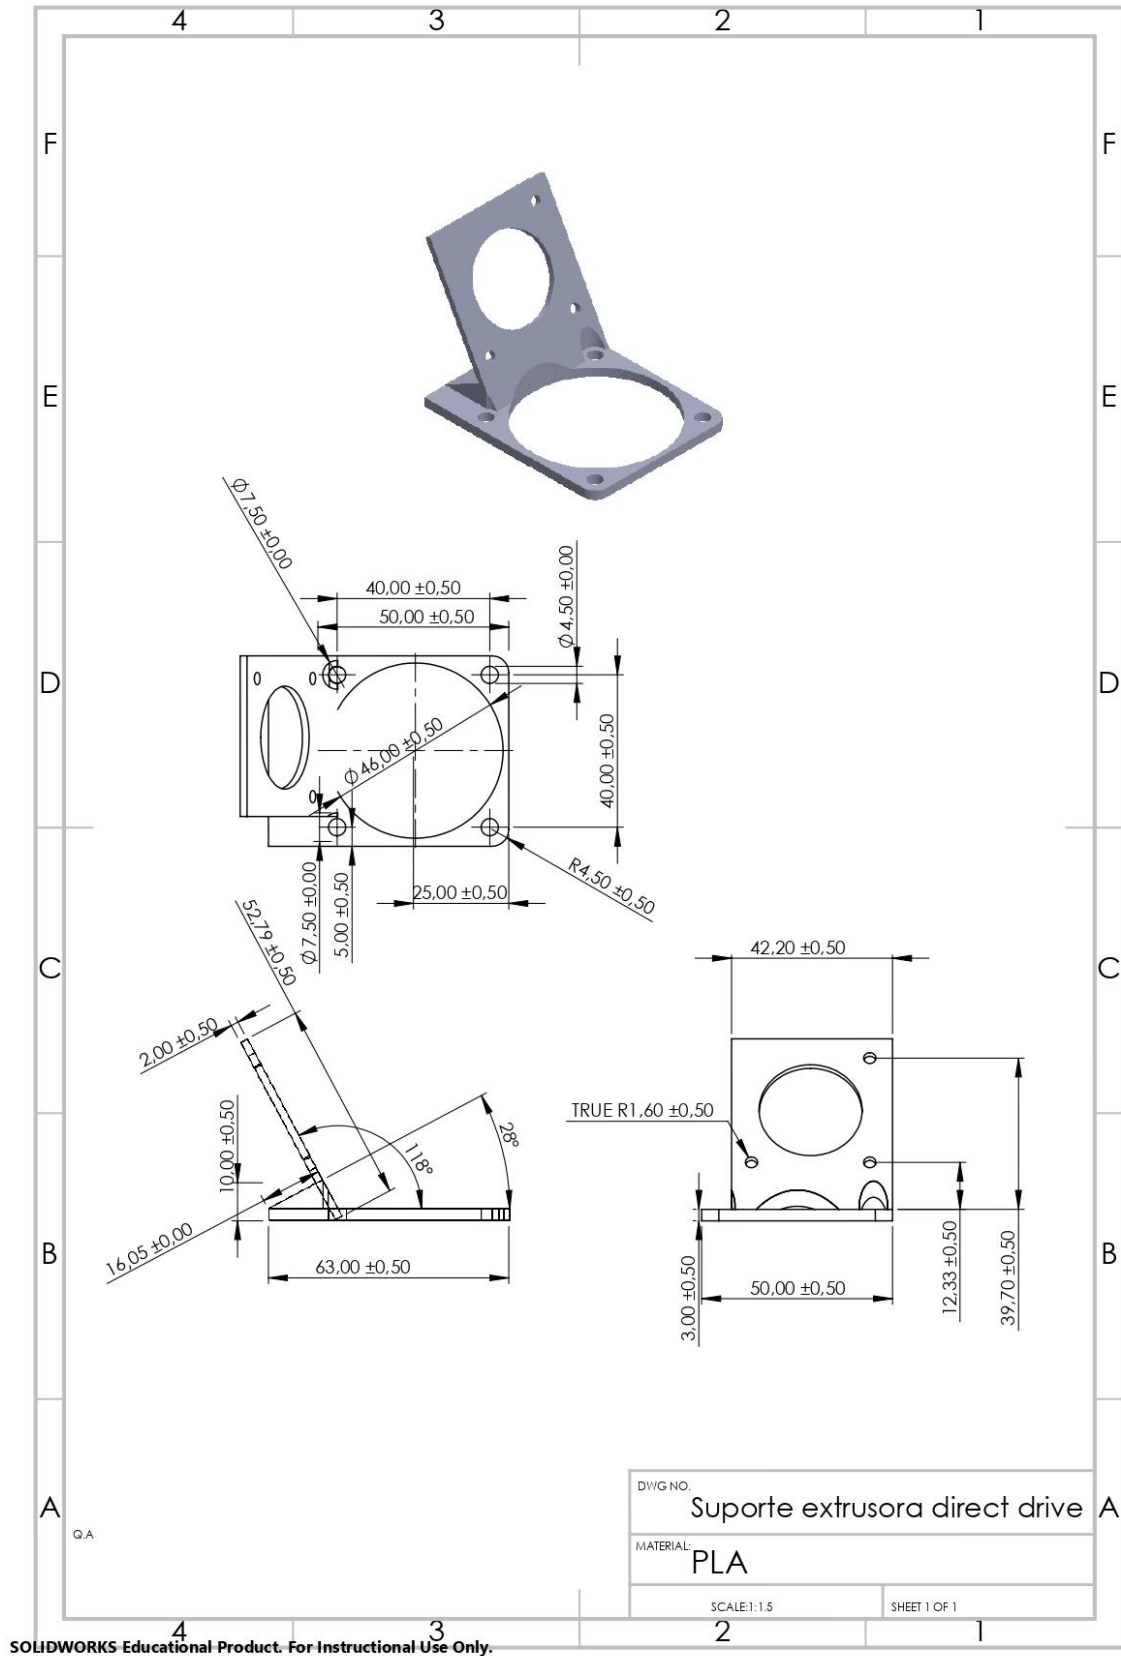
Desenho técnico do suporte extrusora *direct drive*.
